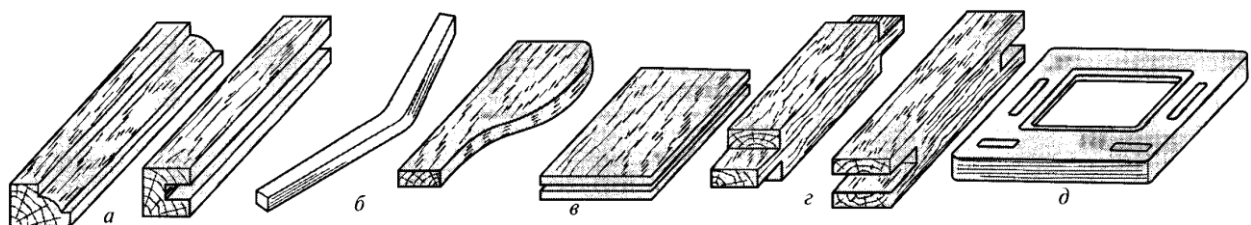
Види обробки на фрезерних верстатах: а – поздовжнє профільне фрезерування; б – криволінійне фрезерування; в – обробка по контуру; г – фрезерування шипів; д – профільне фігурне фрезерування
